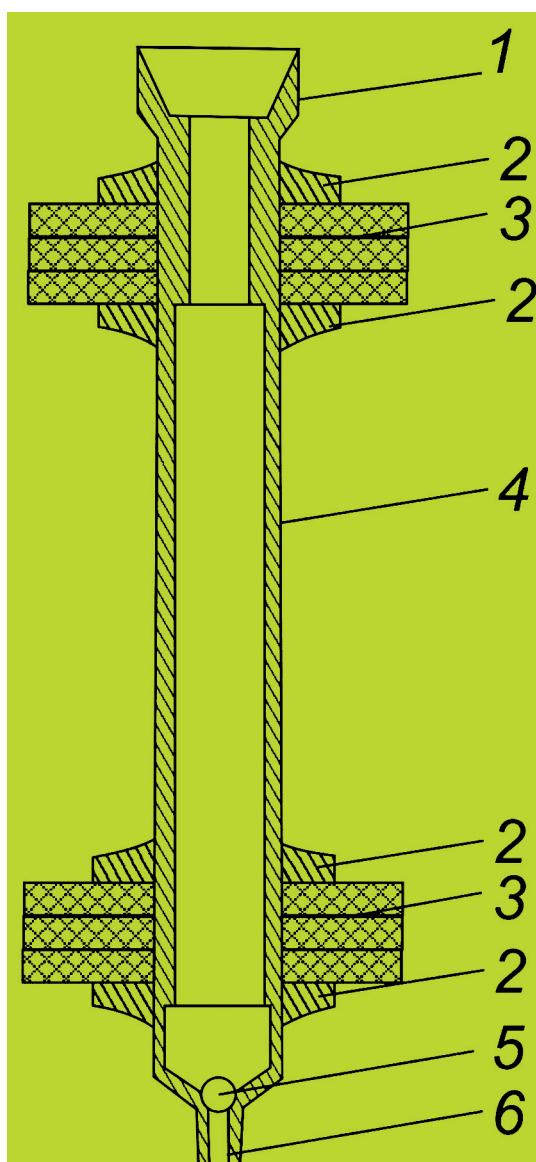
Двойной сваб-пакер: 1 — переходник; 2 — шайба металлическая; 3 — резиновые манжеты; 4 — перфорированный патрубок; 5 — металлический шар; 6 — переходник
